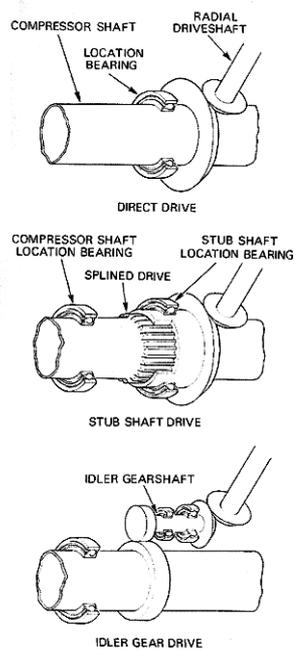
". - Acoplamiento mecánico internos de cajas de engranajes.
